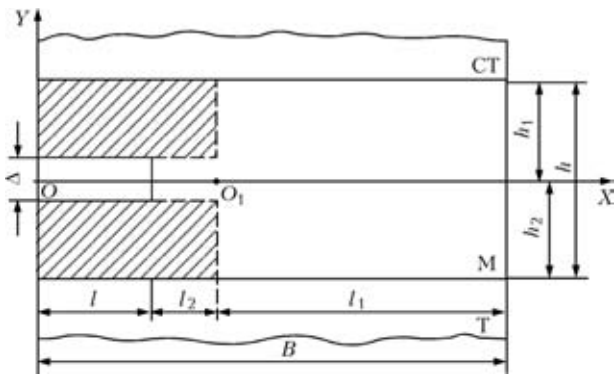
Параметры мягкой прослойки с несимметричной механической неоднородностью и поверхностным трещиноподобным дефектом сварного шва (обозначения см. в тексте)
